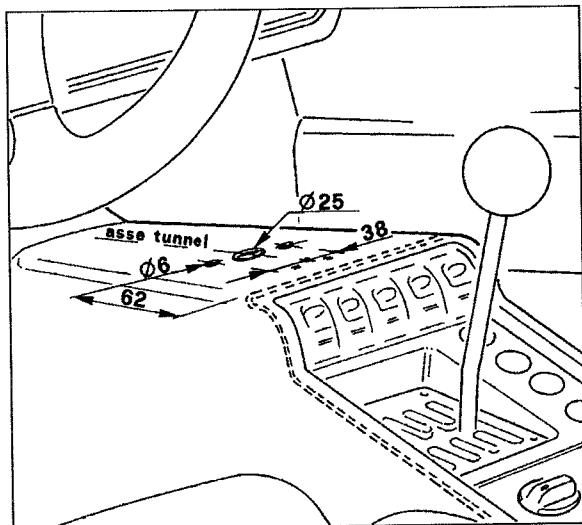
Foratura tunnel per fissaggio staccabatteria
